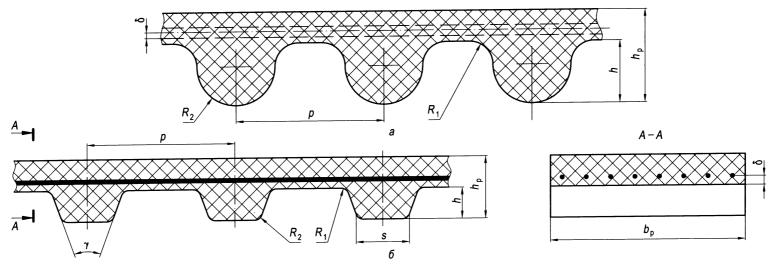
Зубчатые ремни с полукруглым (a) и трапецеидальным (δ) профилем зубьев
